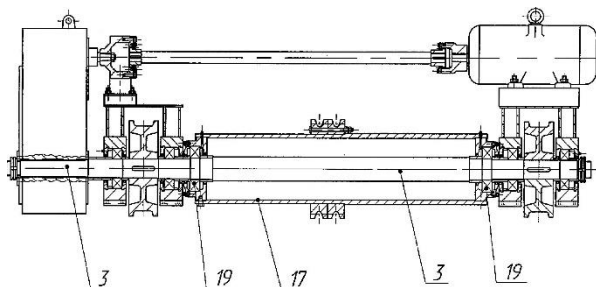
Сечение Б-Б грузовой тележки: 3 – вал; 17 – труба; 19 – подшипники
